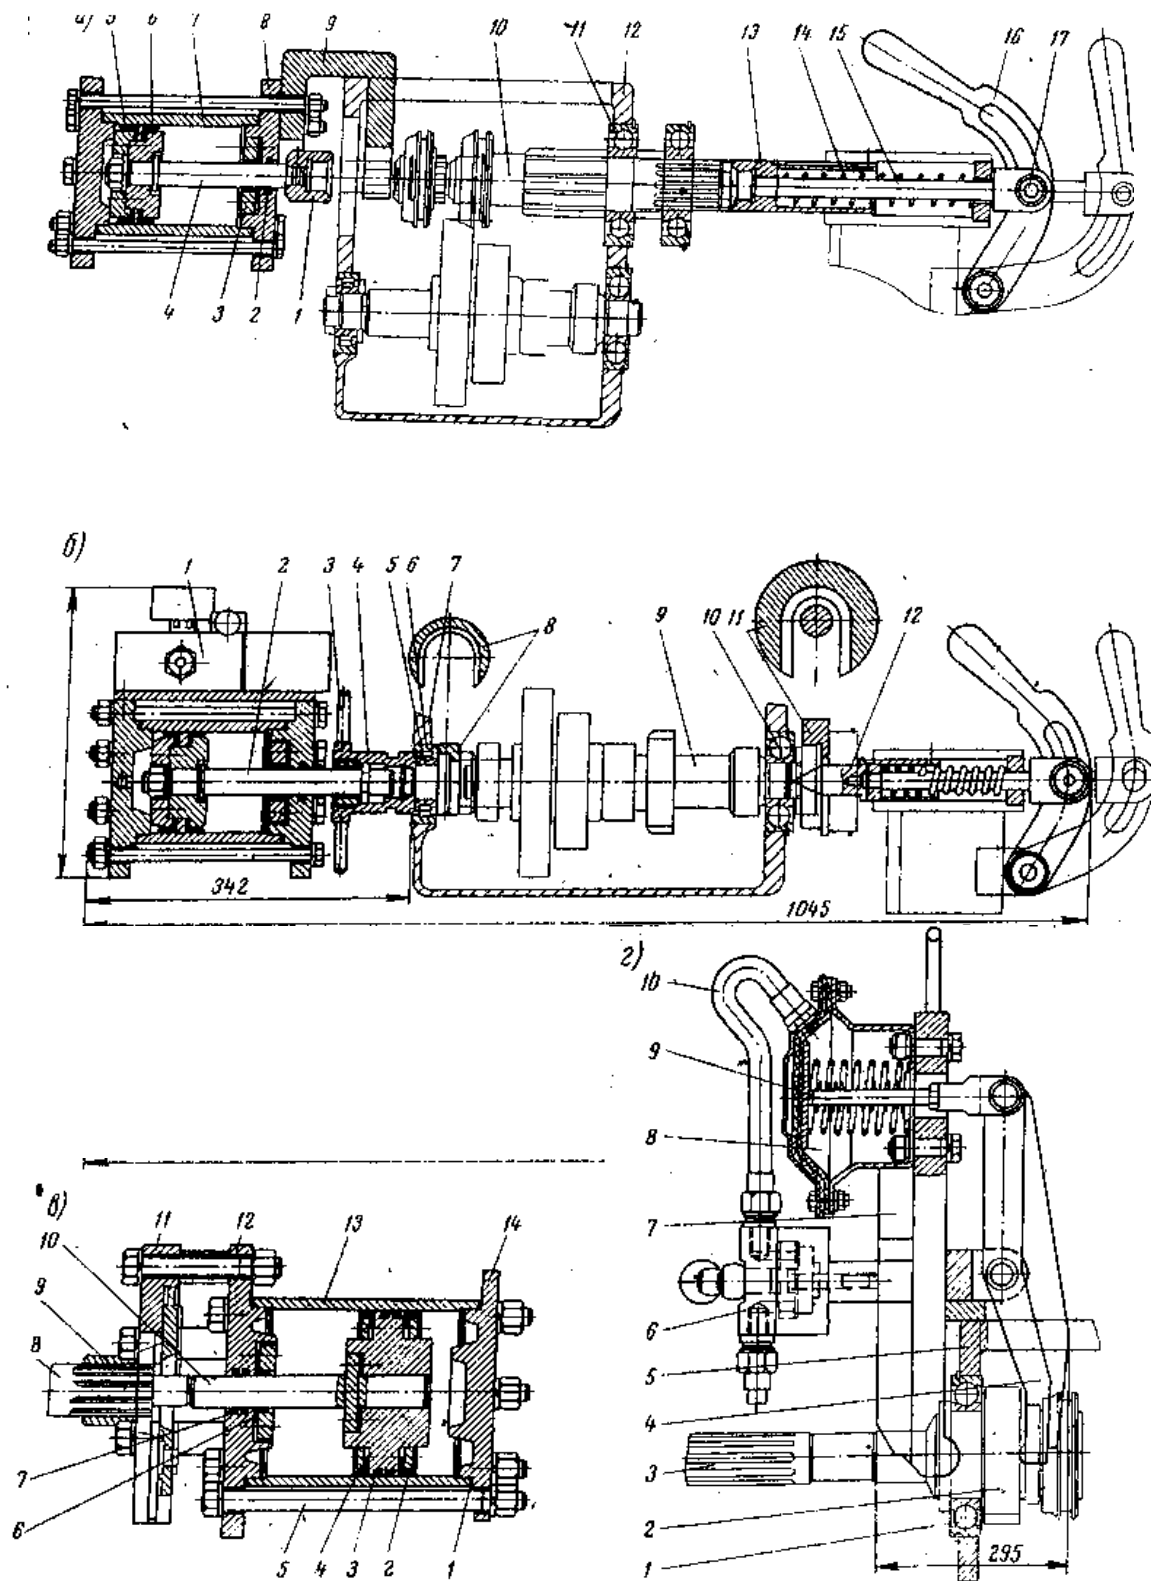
Пристрій для випресування вал-шестерні головної передачі4
